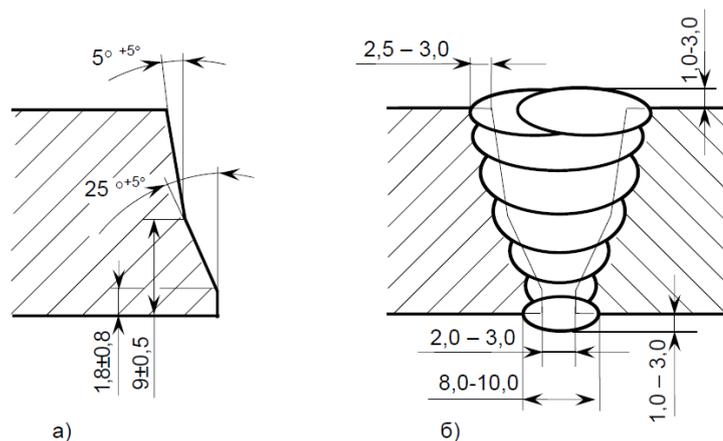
Геометрические параметры специальной разделки кромок труб [9]: (а) и сварного шва (б) неповоротных кольцевых стыковых соединений труб, выполненных механизированной сваркой самозащитной порошковой проволокой
